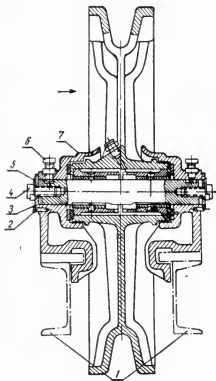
Схема регулировки направляющих колес тракторов КД-35, КДП-35 и Т-28:
